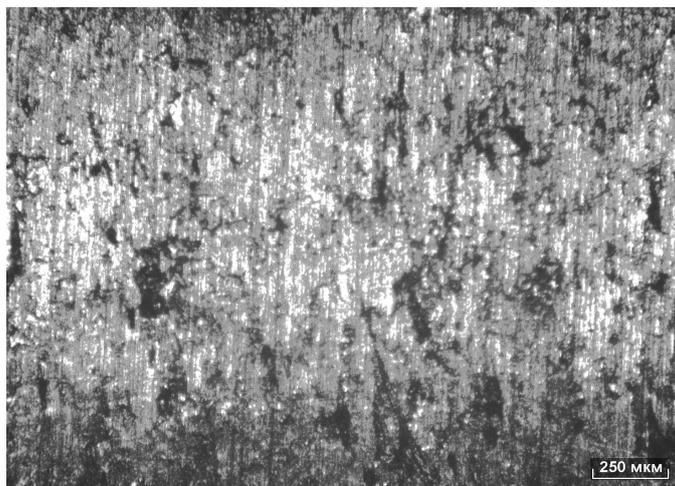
Поверхность металлокерамики типа BrOgr после лезвийной обработки быстрорежущей сталью ( $\times 250$ )
